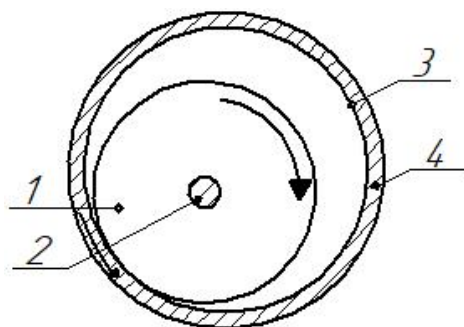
Почвообрабатывающий каток с фрикционно-планетарным вибровозбудителем с наружной обкаткой: 1 – гладкий цилиндр; 2 – оси; 3 – беговая поверхность движения; 4 – пустотелого цилиндра
